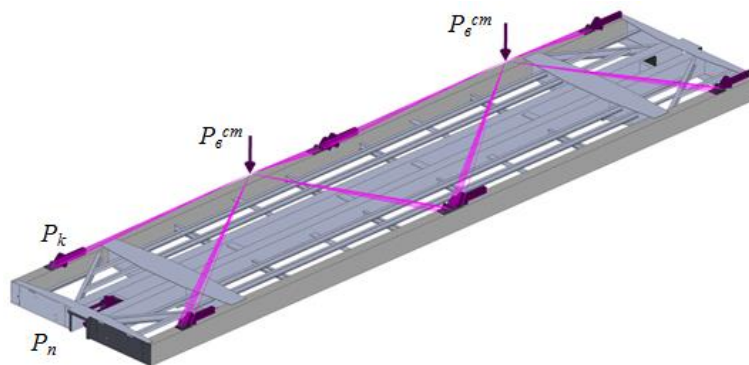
Розрахункова схема несучої конструкції вагона-платформи
